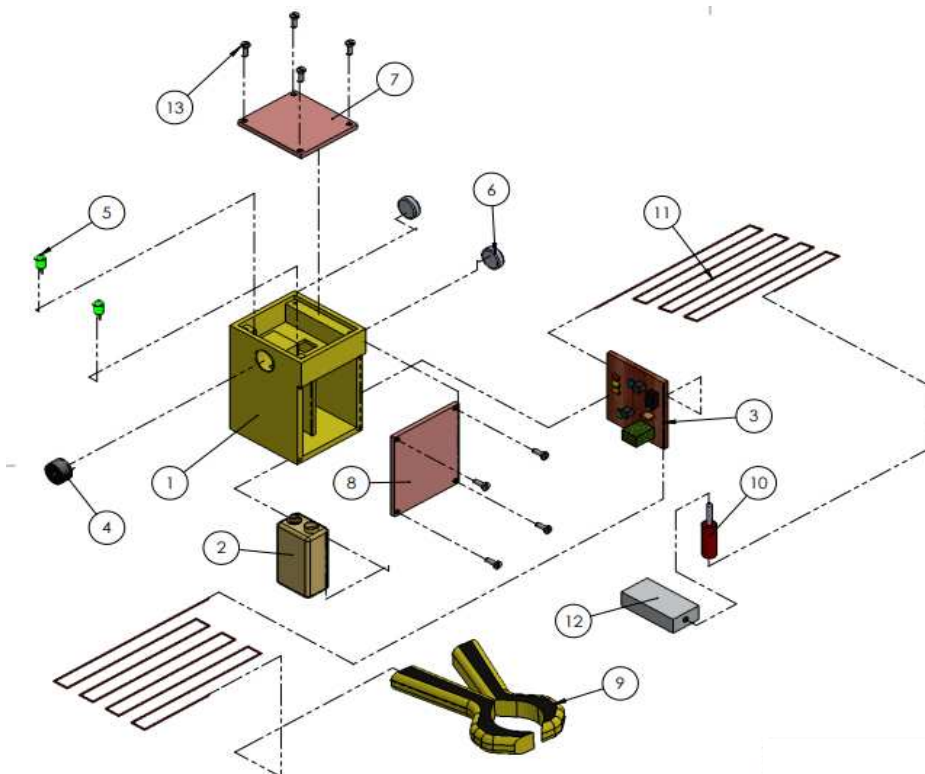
Vista explosionada del calibrador (Fuente: Propia).
